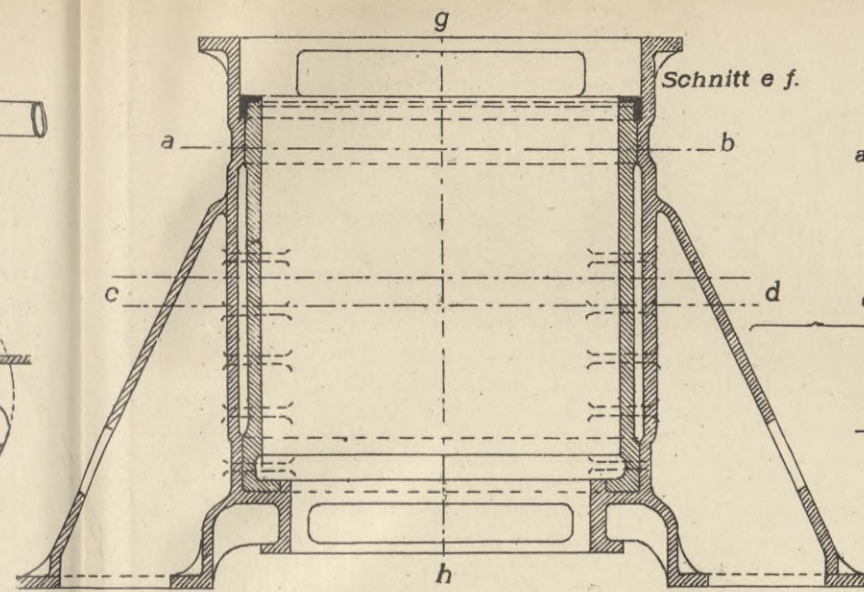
Längsschnitt durch die Cylinder einer Dreifach-Expansionsmaschine.
